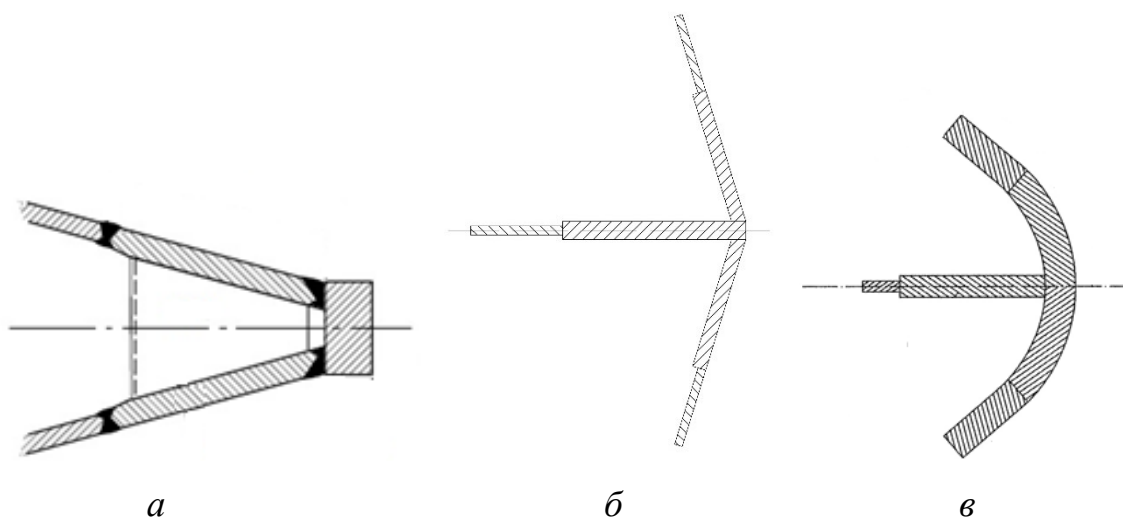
Сечения форштевней: *a* – брускового сварного с острыми кромками; *б* – листового сварного с острыми кромками; *в* – листового сварного с профилированным листом.
